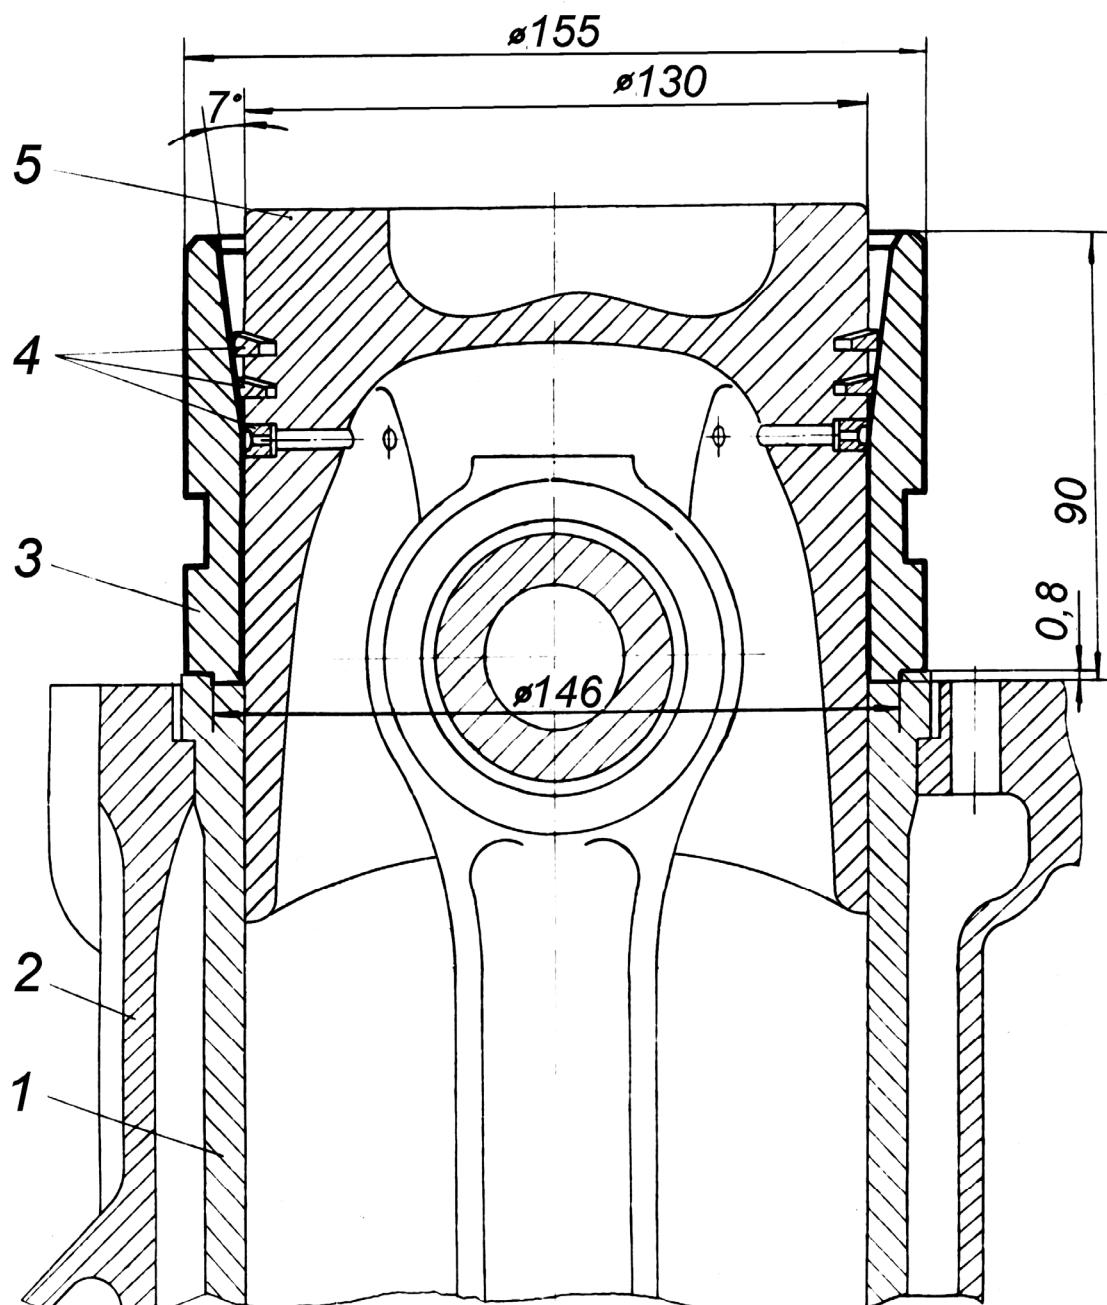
Оправка для установки поршня в гильзу цилиндра
